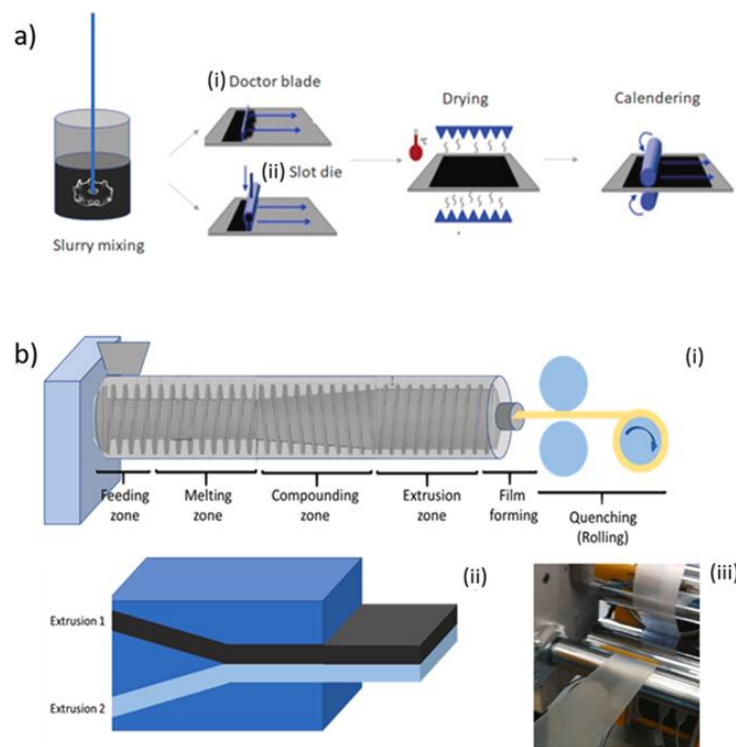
Procédés en voie liquide : (a) slurry ; (i) tape casting (doctor blading) ; (ii) slot-die coating ; (b) (i) melt extruder ; (ii) co-extrusion ; (ii) polymère extrudé après calandrage [193]
